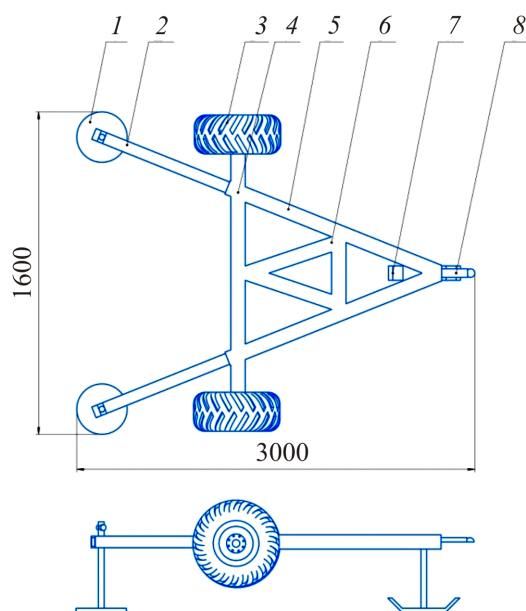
Схема несущей платформы типа «треугольник»: 1 – опорный диск; 2 – выносная опора; 3 – колесо; 4 – фиксатор; 5 – внешняя рама; 6 – каркас усиления рамы; 7 – опорная лыжа; 9 – фаркоп
